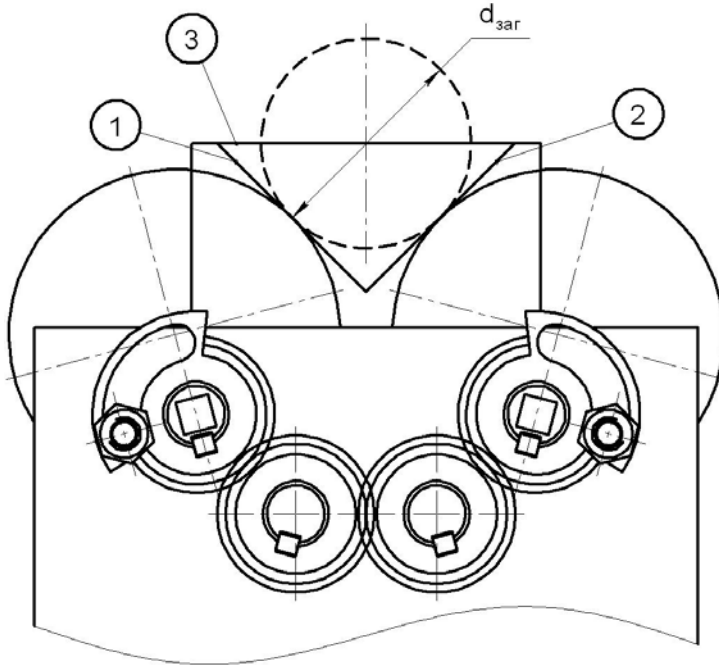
Налаштування базуючої призми за допомогою шаблона-установки: поверхні 1 та 2 – відповідають діаметру заготовки; поверхня 3 – для налаштування різального інструменту
